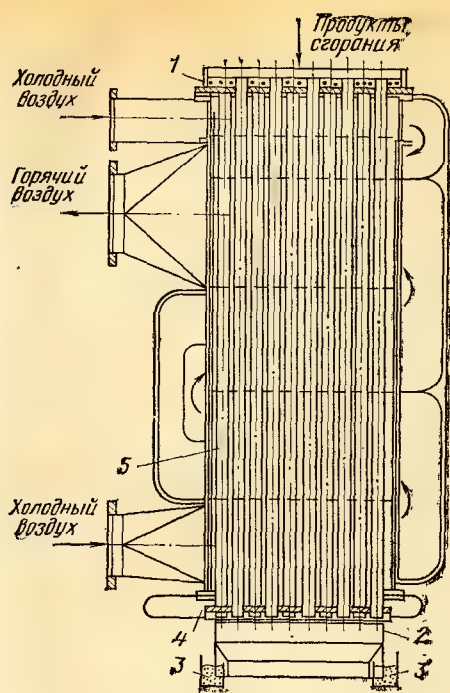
Трубчатый конвективный рекуператор для нагревательных печей:
